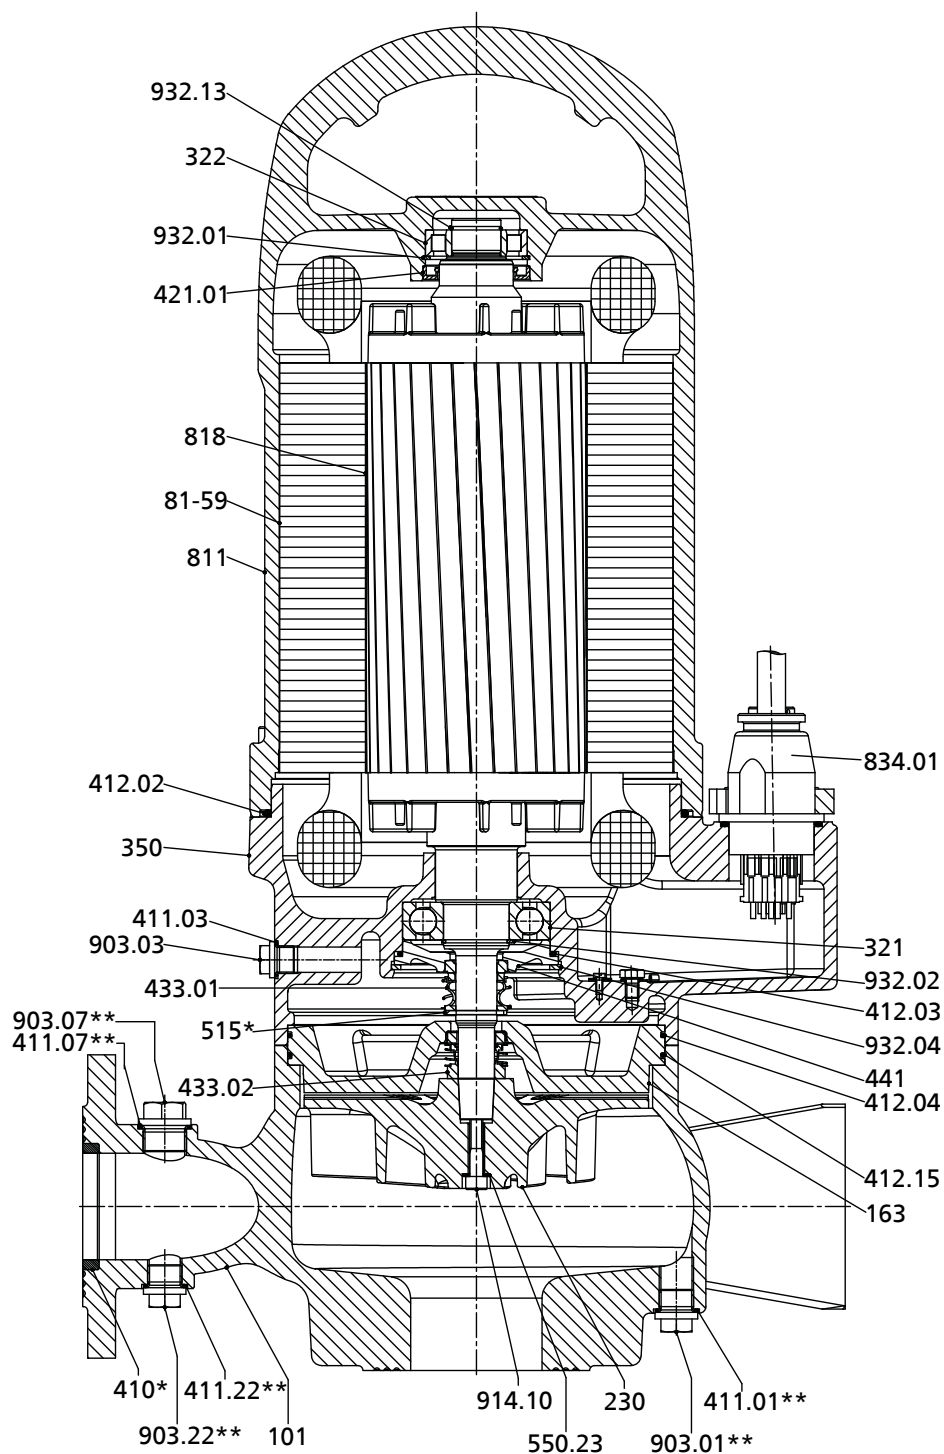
Сборочный чертеж Amarex KRT, тип двигателя 2
